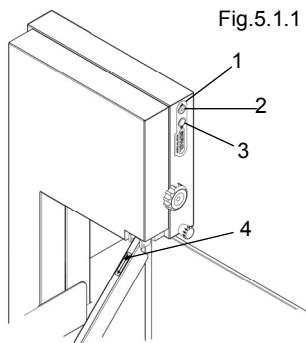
Posicionar el interruptor diferencial que está instalado arriba de la máquina, en la posición "I". El indicador luminoso "2" debe estar iluminado. Seleccionar con el selector la velocidad para hacer girar el motor. Pulsar el botón "1" de marcha y enseña después el botón "3" de parada controlando la dirección de la hoja. La dirección de la hoja debe coincidir con el que indica la flecha "4" Fig. 5.1.1,), o sea hacia el plano de trabajo. Si la dirección de rotación es contraria, desconectar el interruptor diferencial llevándolo a la posición "0". de esta manera se ha desconectado la alimentación eléctrica.
